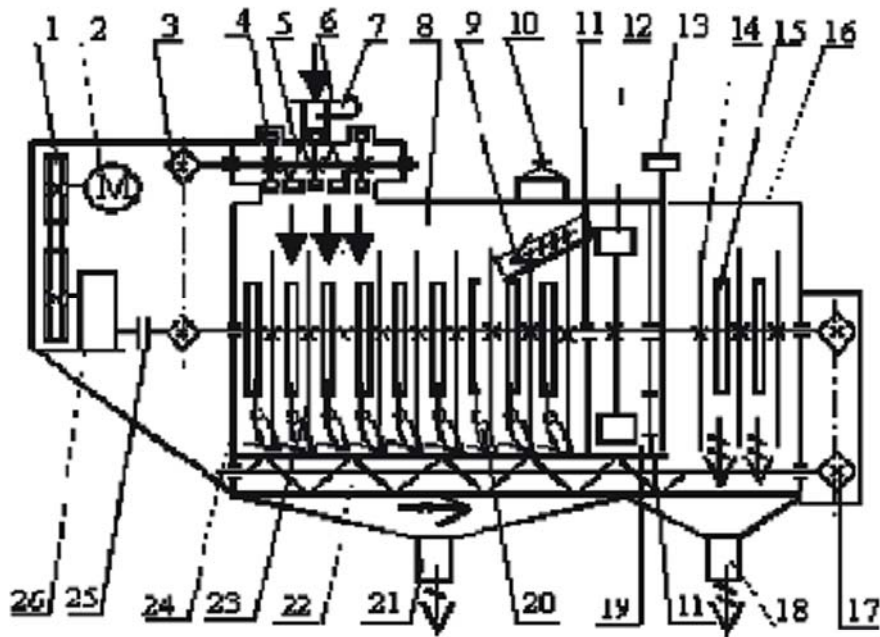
Схема трієра кукілевідбірника типу А9-УТК: 1 - пасова передача; 2 - електродвигун; 3 - ланцюгова передача приводу ЖП; 4 - ковшове колесо ЖП; 5 – живильний шнек; 6 - приймальний патрубок; 7 - заслонка ЖП; 8 - робоче відділення; 9 - лоток перевантажувального пристрою; 10 - аспіраційний патрубок; 11 - перегородка; 12 - ковшове колесо перевантажувального пристрою; 13-заслонка КВ; 14 - диск КВ; 15 - лоток КВ; 16- КВ; 17 - ланцюгова передача приводу шнека для короткої фракції; 18 - патрубок для випуску короткої фракції; 19 - перевантажувальне відділення; 20 - корпус; 21 - патрубок для випуску очищеного зерна; 22 - шнек; 23 - диски робочого відділення; 24 - лотки; 25 - ланцюгова муфта; 26 - редуктор.
